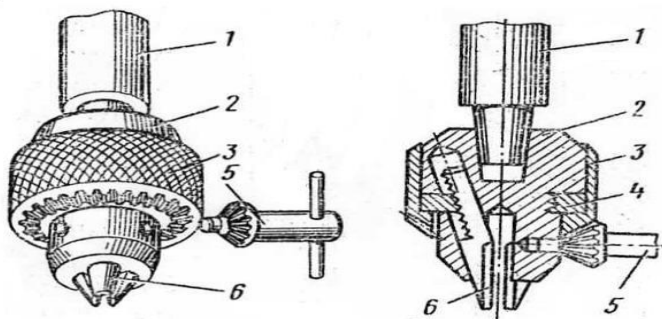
Сверлильный кулачковый патрон с ключом: *а* – общий вид патрона, *б* – осевое сечение
